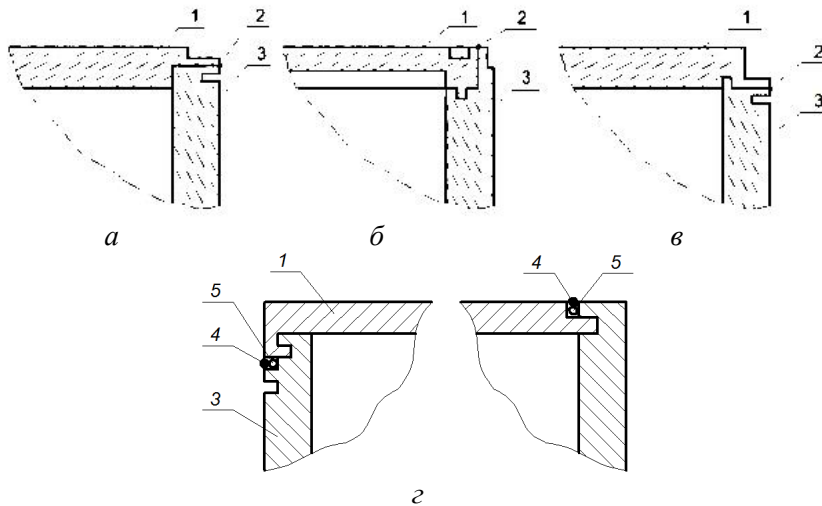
Схеми вузлів герметизації корпусів: 1 – кришка; 2 – зварний шов; 3 – стінки корпусу; 4 – герметик або паяний шов; 5 – дріт для розкриття
